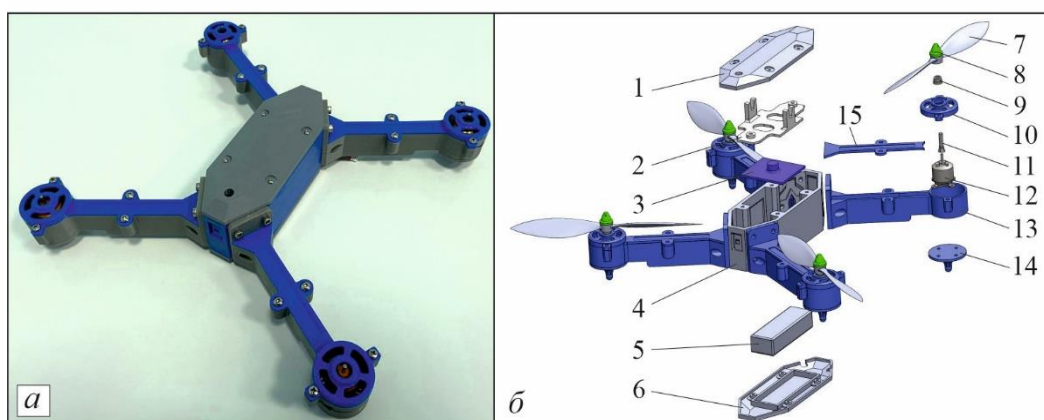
Малоразмерный БПЛА: (а) – Общий вид; (б) – Кон-струкция: 1 – верхняя крышка, 2 – верхняя подставка; 3 – нижняя подставка; 4 – корпус; 5 – аккумулятор; 6 – нижняя крышка; 7 – про-пеллер; 8 – колпак двигателя; 9 – втулка; 10 – крышка двигателя; 11 – накидной болт; 12 – бесколлекторный двигатель; 13 – рама крыла; 14 – подставка двигателя.
